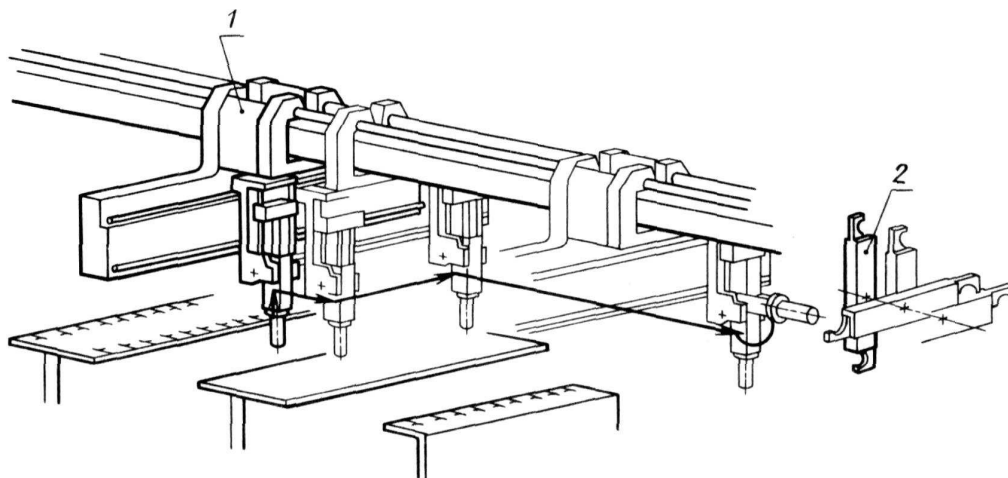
Транспортное приспособление и автооператор смены инструмента при кассетном магазине инструментов
